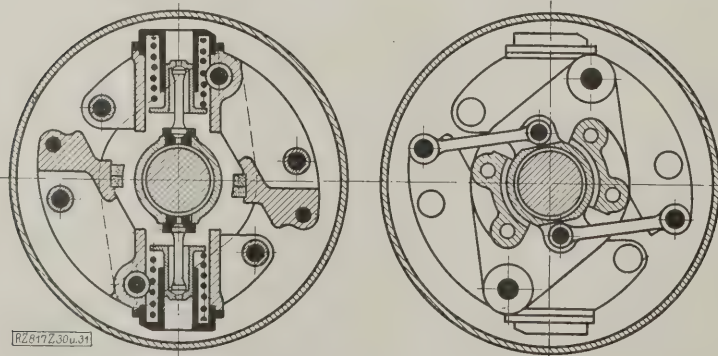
und 31. Schnitt durch die Gewichte des Achsreglers.
